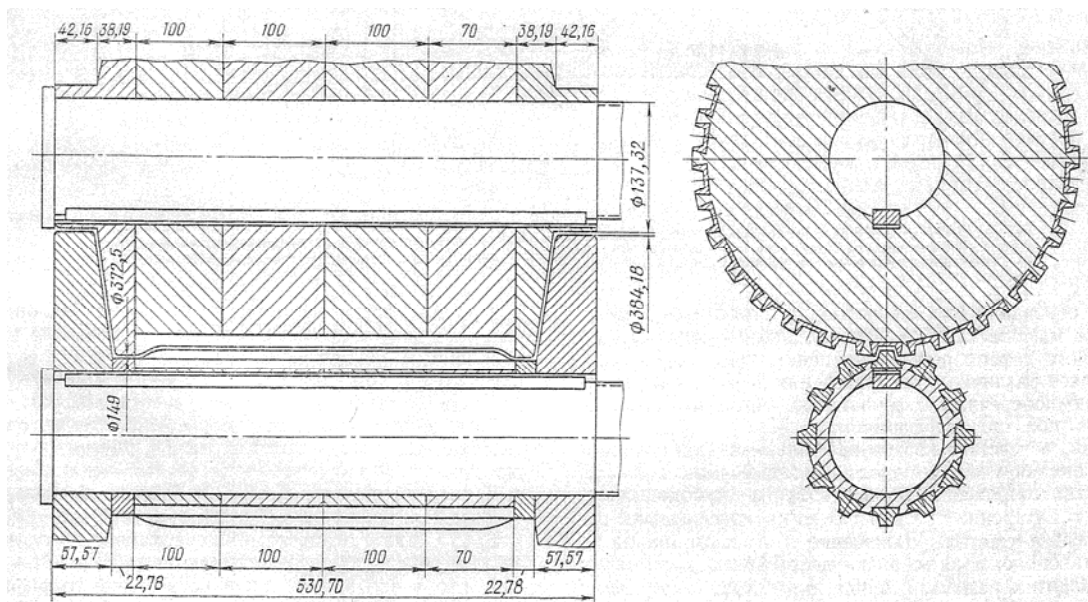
Конструкция валков клетки 8 профилегибочного стана, где формируются поперечные гофры противоскольжения
